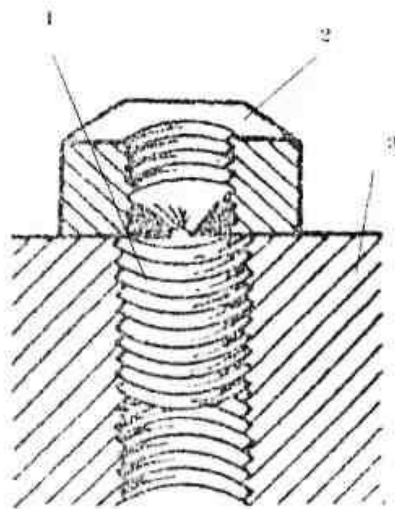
Приварена гайка: 1- шпилька; 2- гайка; 3- деталь
